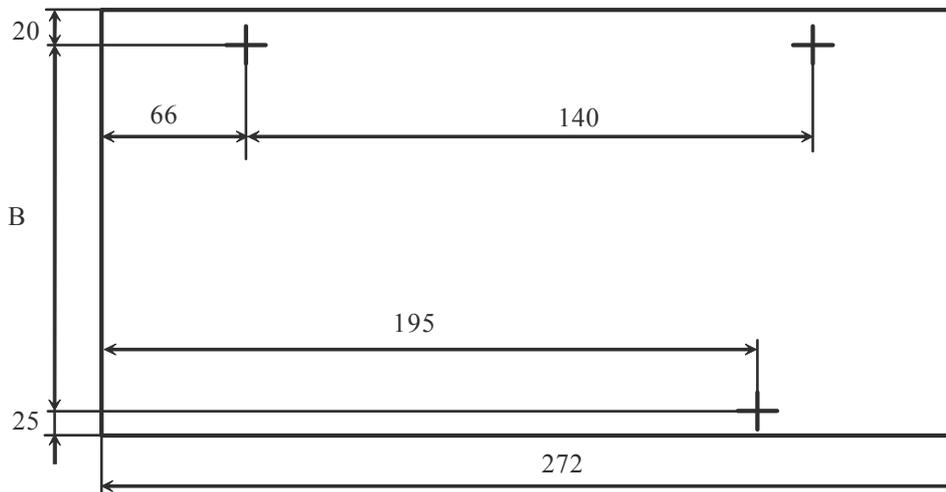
Разметка для крепления МБ с МР на стене.
